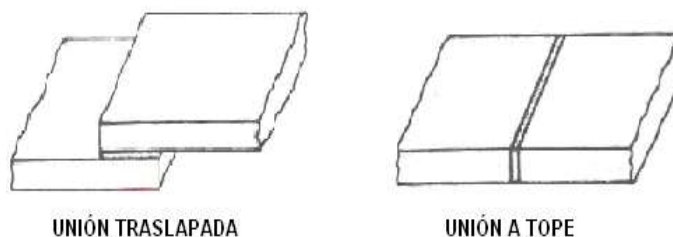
Uniones traslapada y a tope básicas para soldadura fuerte
